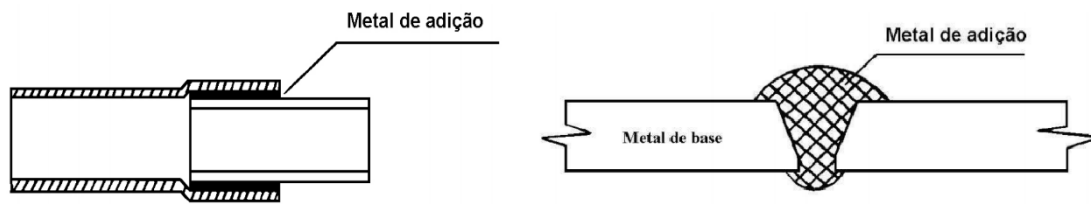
Diferença entre brasagem e soldobrasagem
